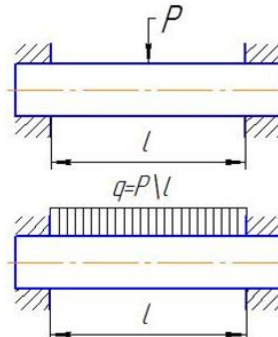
Схеми навантаження брусу, який кріпиться у двох фіксованих опорах
